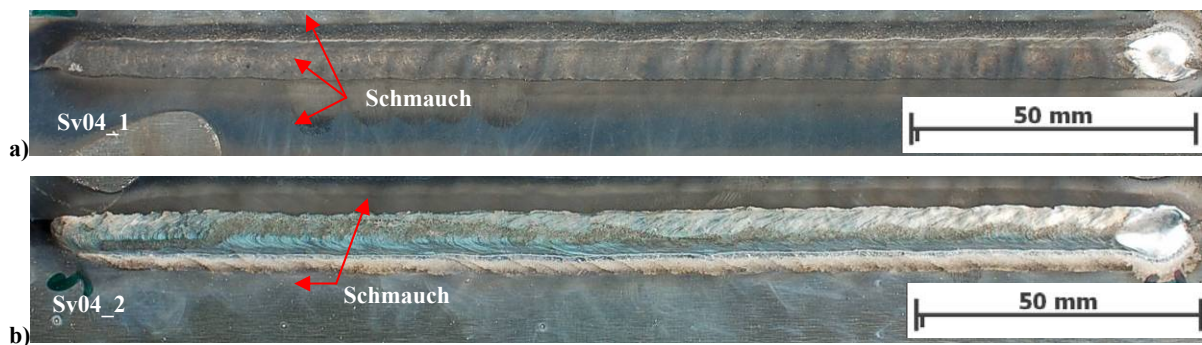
Einfluss des Anstellwinkels auf den Schweißschmauch- Niederschlag beim Schweißen von ungereinigten AW-5083-O Schweißnähten a) 15° schleppend b) 5° stechend
